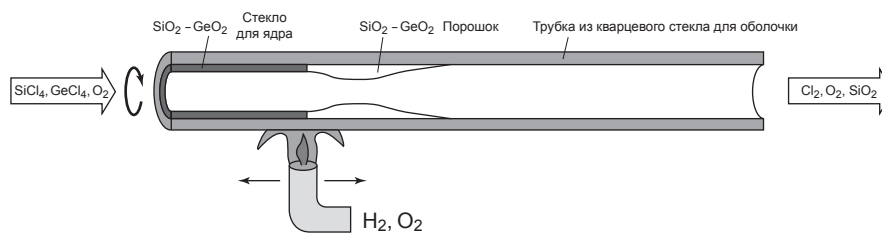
Процесс изготовления заготовки для оптоволокна методом осаждения из газовой фазы
